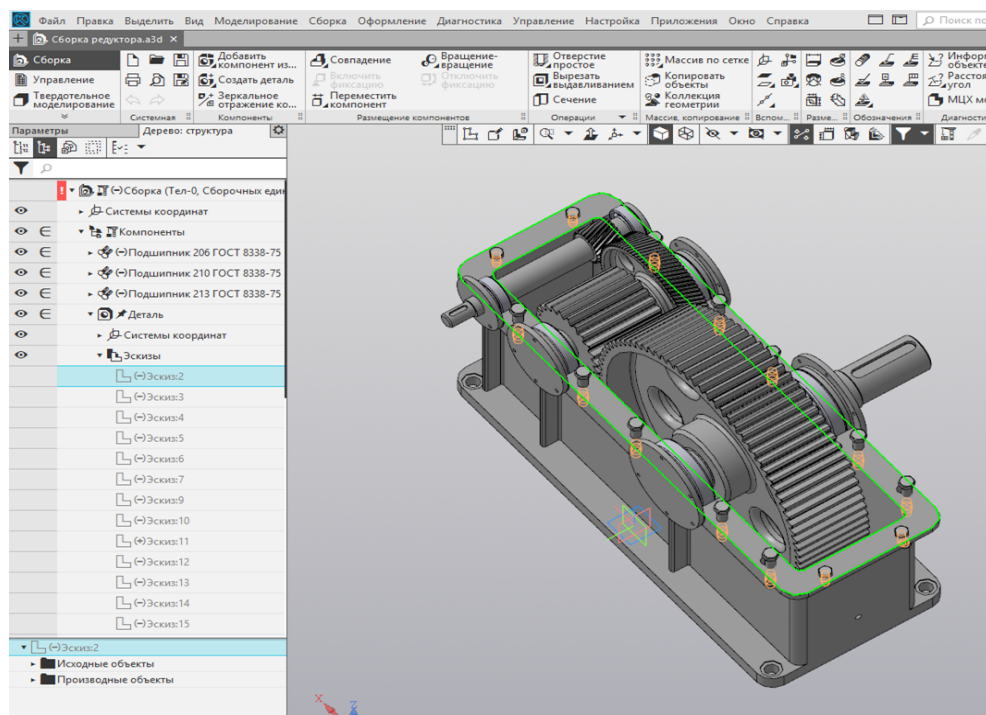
Прив'язка моделі корпусної деталі до початку координат
